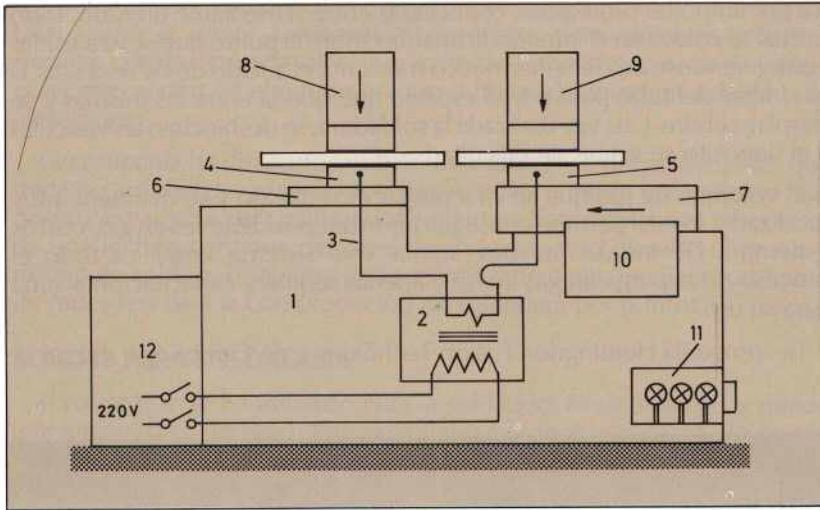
Representación esquemática de una máquina de soldadura a tope.
